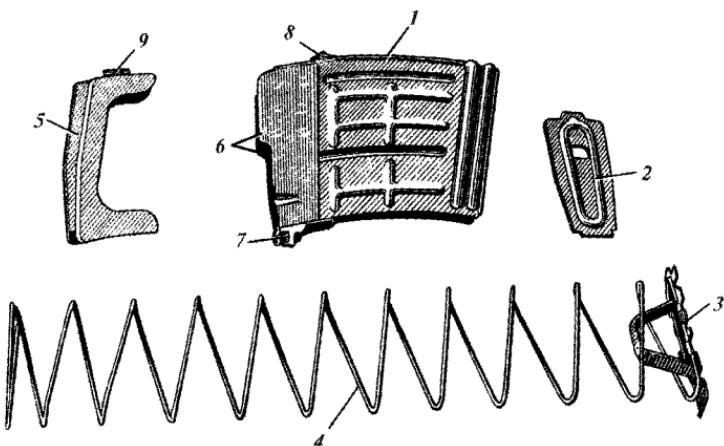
Магазин СВД-63: 1 — корпус; 2 — крышка; 3 — стопорная планка; 4 — пружина; 5 — подаватель; 6 — загибы; 7 — зацеп; 8 — опорный выступ; 9 — выступ подавателя.
